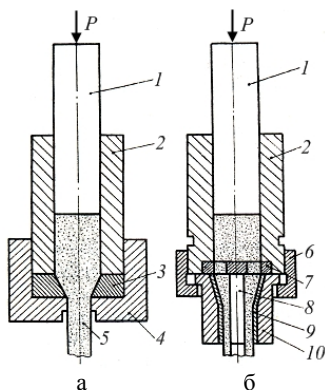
Схема мундштучного прессования стержней (а) и труб (б): 1 — пуансон; 2 — стакан; 3 — конус; 4 — матрица; 5 — спрессованная заготовка; 6 — гайка; 7 — звездочки; 8 — игла; 9 — мундштук; 10 — обойма
